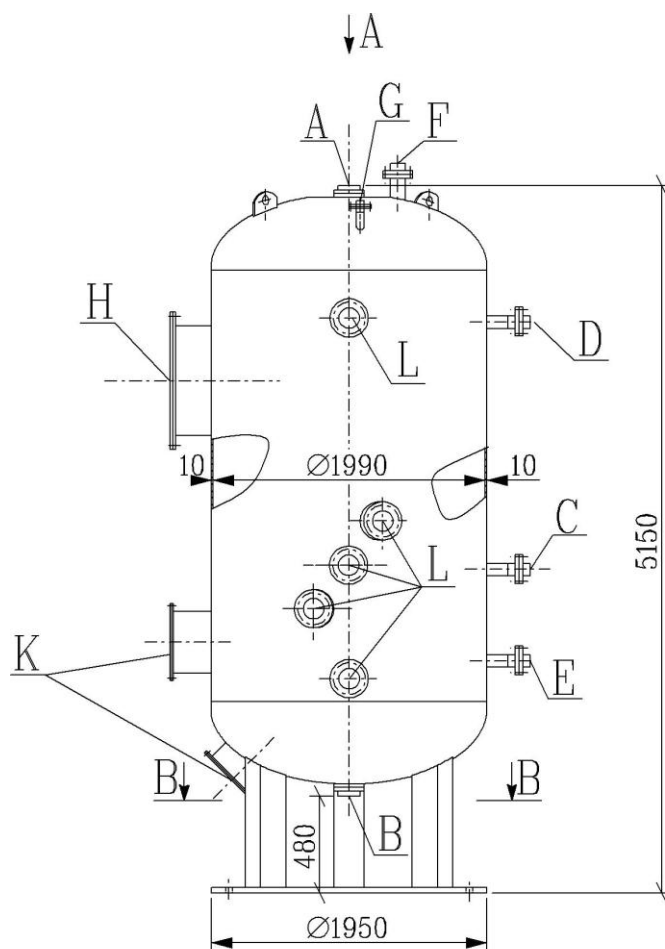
Габаритный чертеж фильтра Н-катионитного обезжелезивающего LDB11AT001, LDB12AT001
